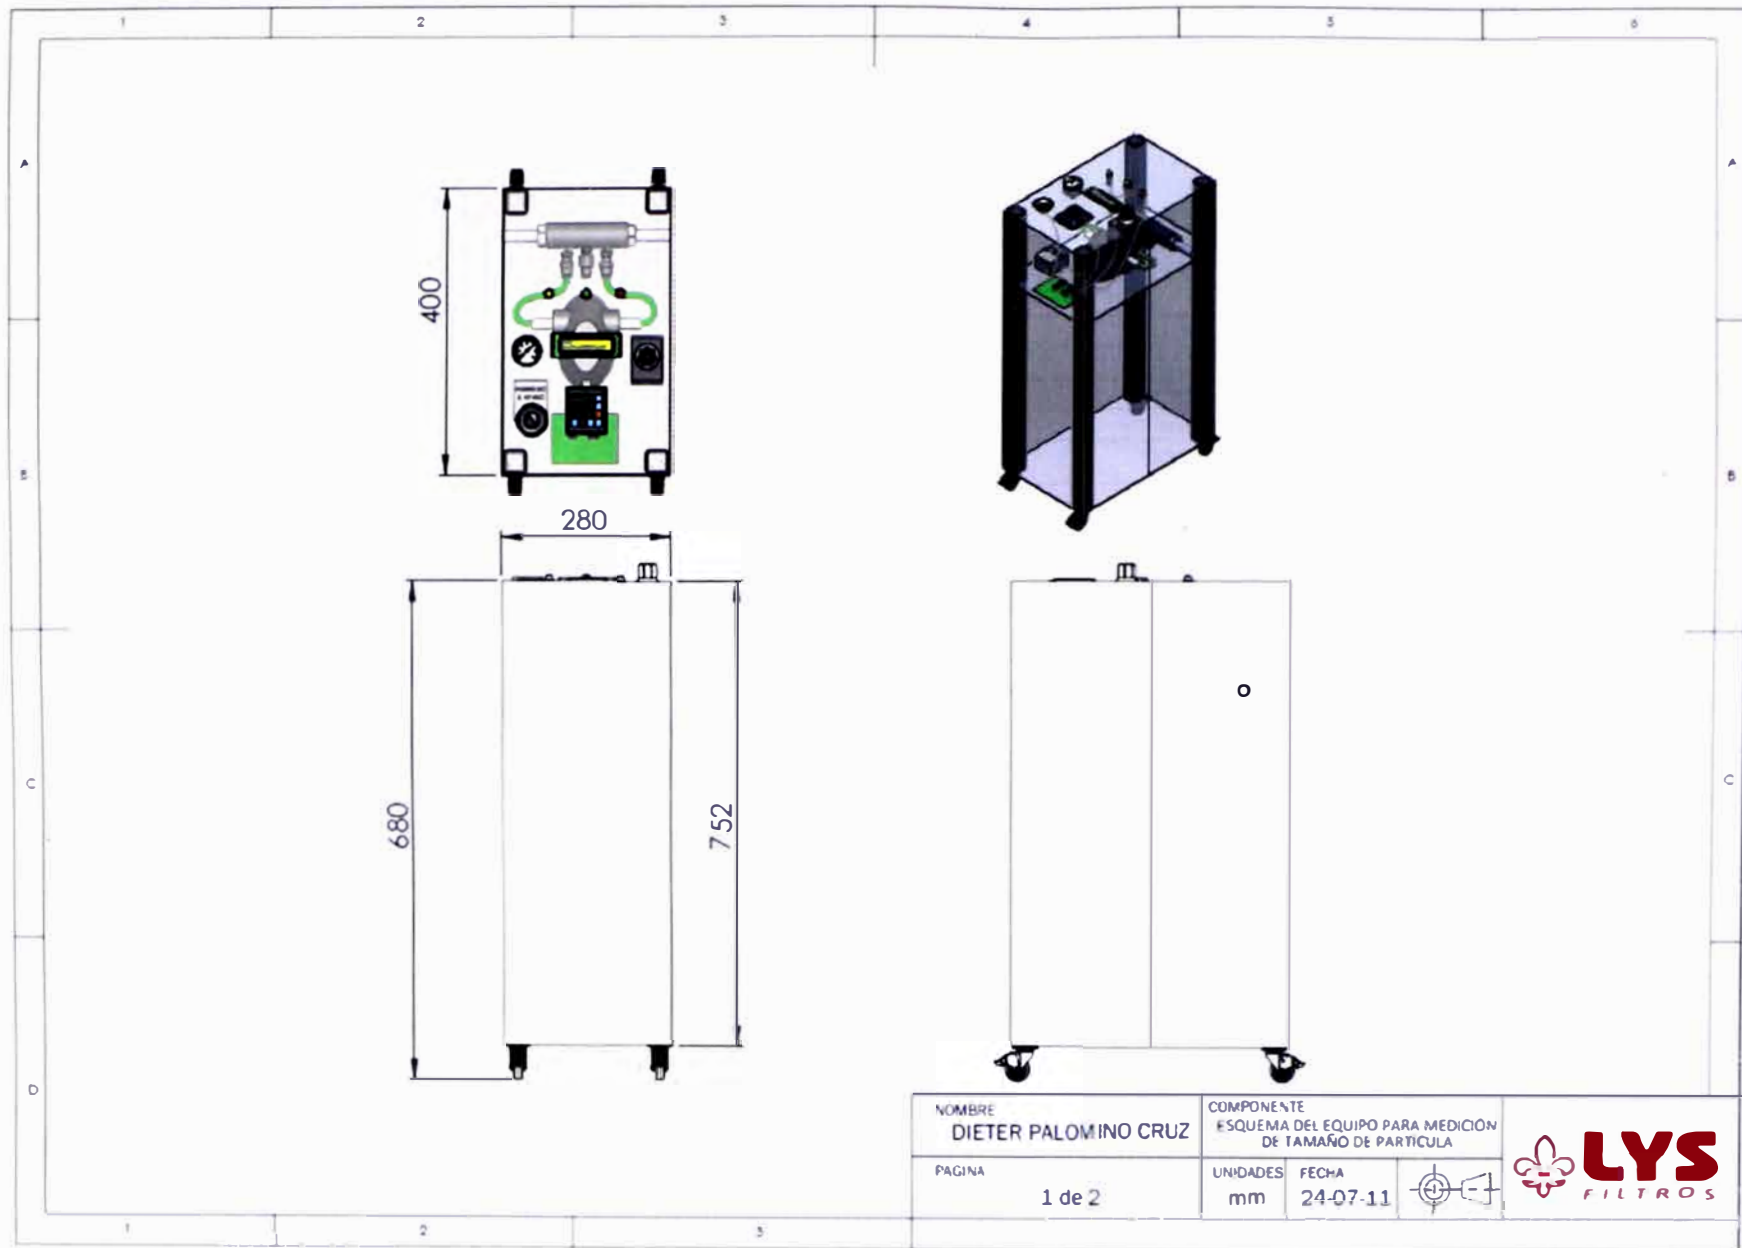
, Plano de ensamble del equipo. Fuente: diseño propio
